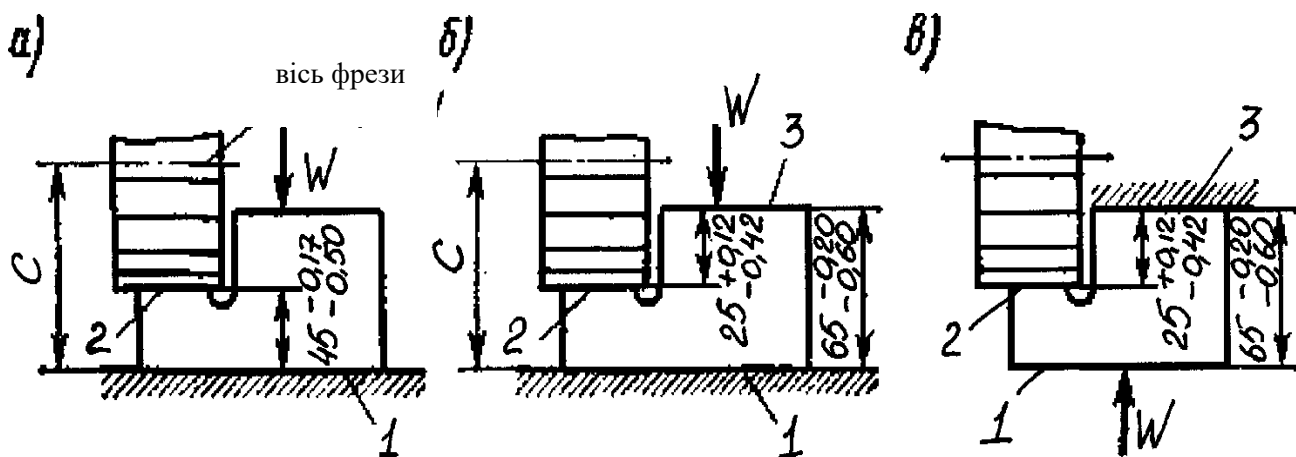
Схеми для визначення похибок базування при установці оброблюваних деталей у пристрої плоскою поверхнею
